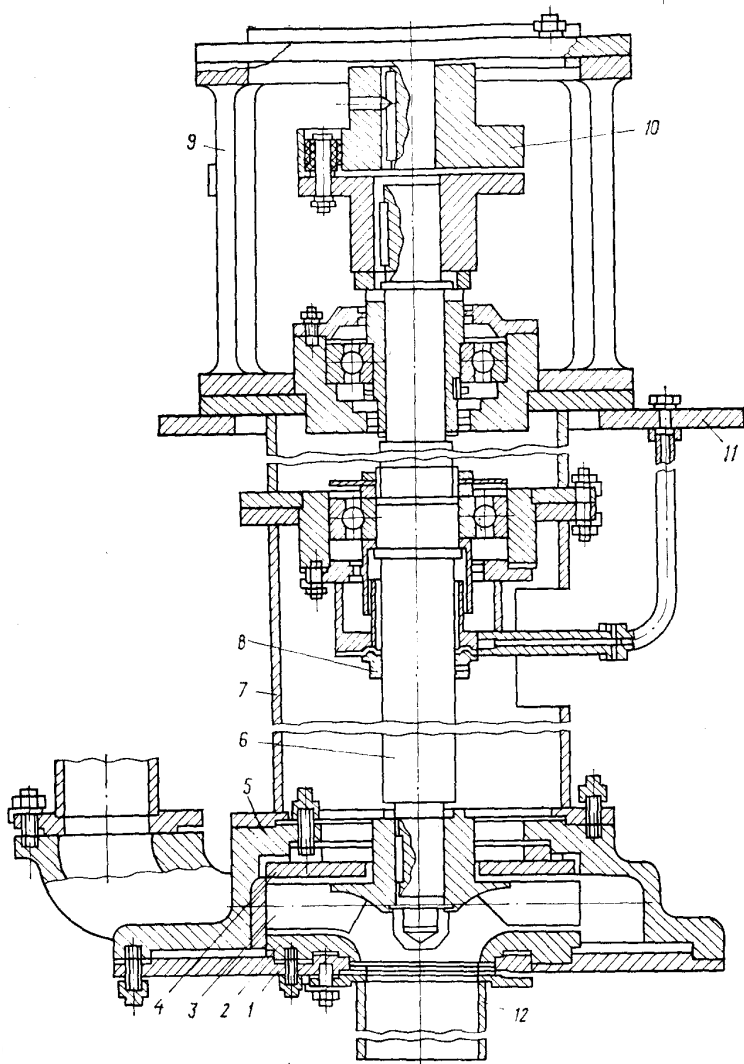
Химические насосы типов ТХИ и АХИ: 1 – крышка; 2 – нижний диск; 3 – рабочее колесо; 4 – верхний диск; 5 – корпус; 6 – вал; 7 – корпус подшипника с подвеской; 8 – отбойник жидкости; 9 – опорная стойка; 10 – муфта; 11 – опорная плита; 12 – всасывающая труба
